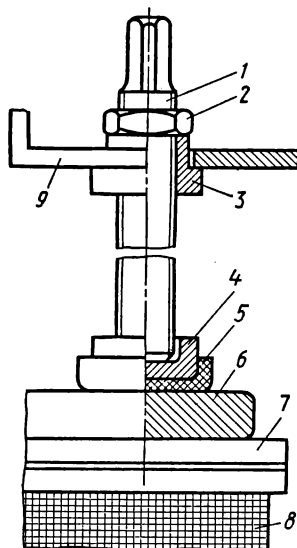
Прессовка обмоток кольцами и нажимными винтами
